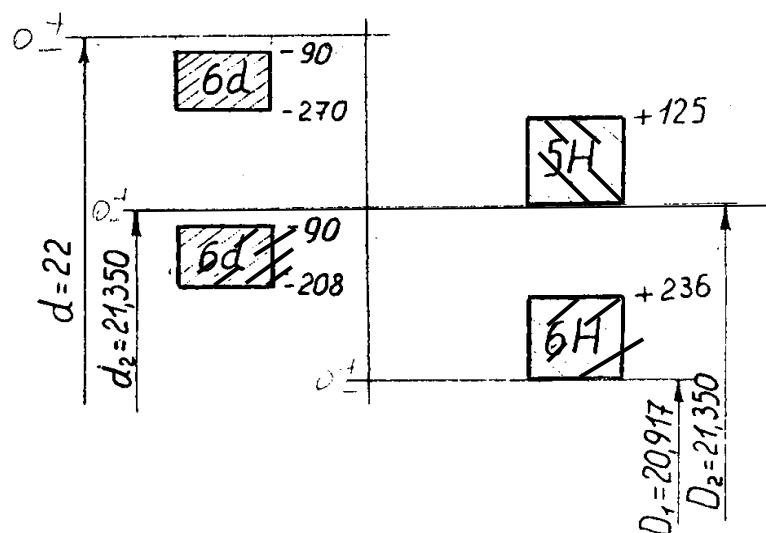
Схема расположения полей допусков метрической резьбы с посадкой с зазором
